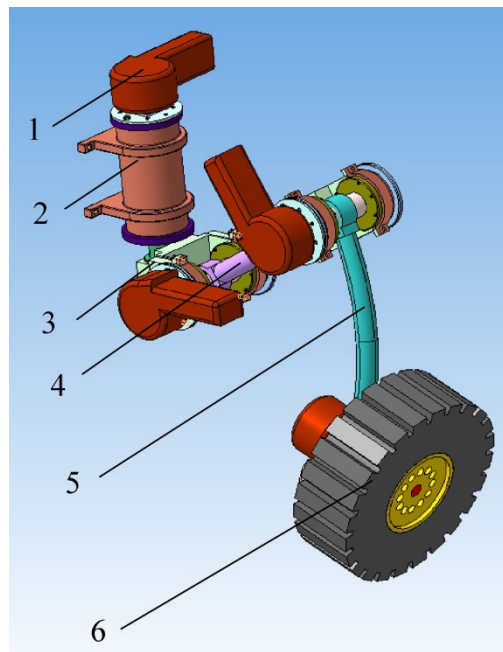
Мехатронный колесно-шагающий модуль. 1 – мотор-редуктор, 2, 4, 5 – жесткое звено, 3 – шарнир, 6 – мотор-колесо с тормозом.
